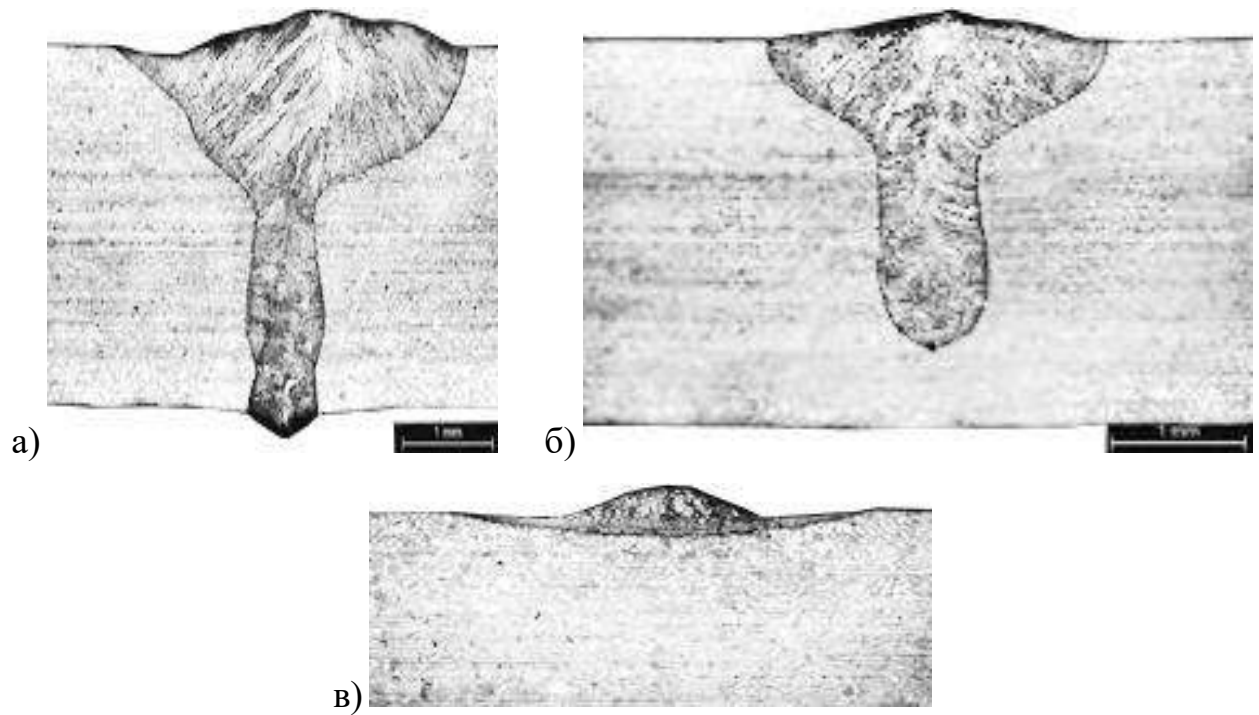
Зовнішній вигляд макрошліфів проварів, виконаних на сталі AISI 304 товщиною 3 мм: а) – гібридним зварюванням (зразок 1); б) – лазерним зварюванням (зразок 2); в) – плазмовим зварюванням (зразок 3)
